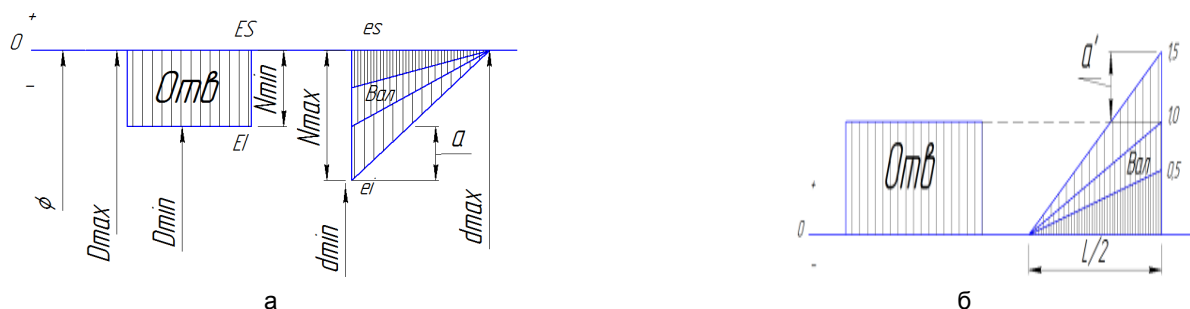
Схема полей допусков для конической пружины: а – сопряжение пружины и отверстия; б – сопряжение пружины и вала
